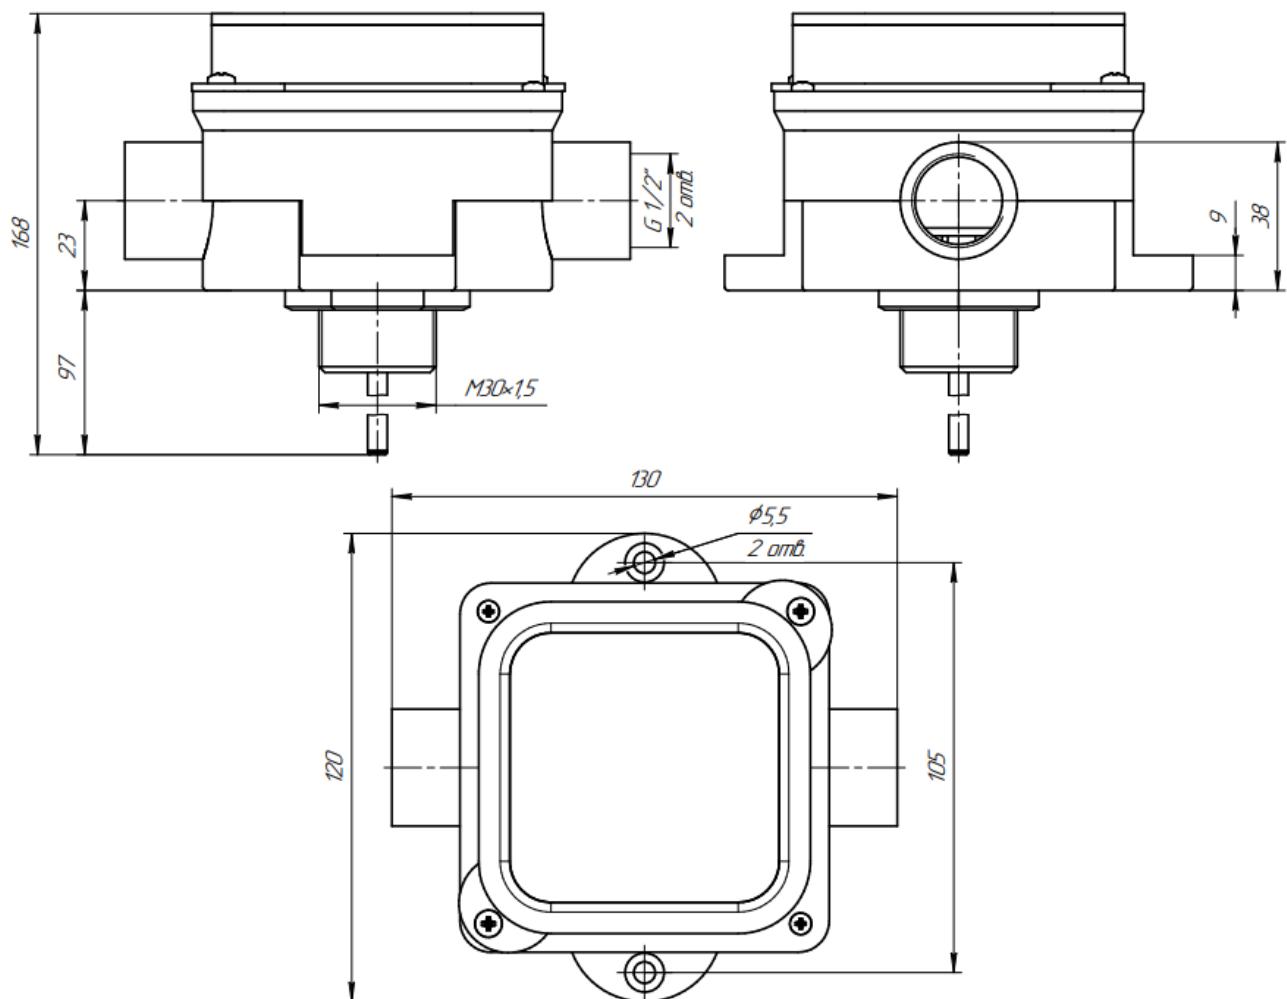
Габаритный чертеж на Спектрон-101-Р-Exi/Exm
